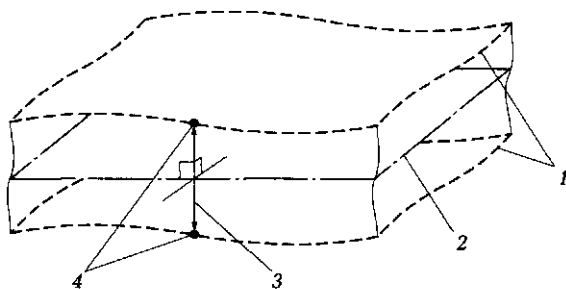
Местный размер двух параллельных выявленных поверхностей:
